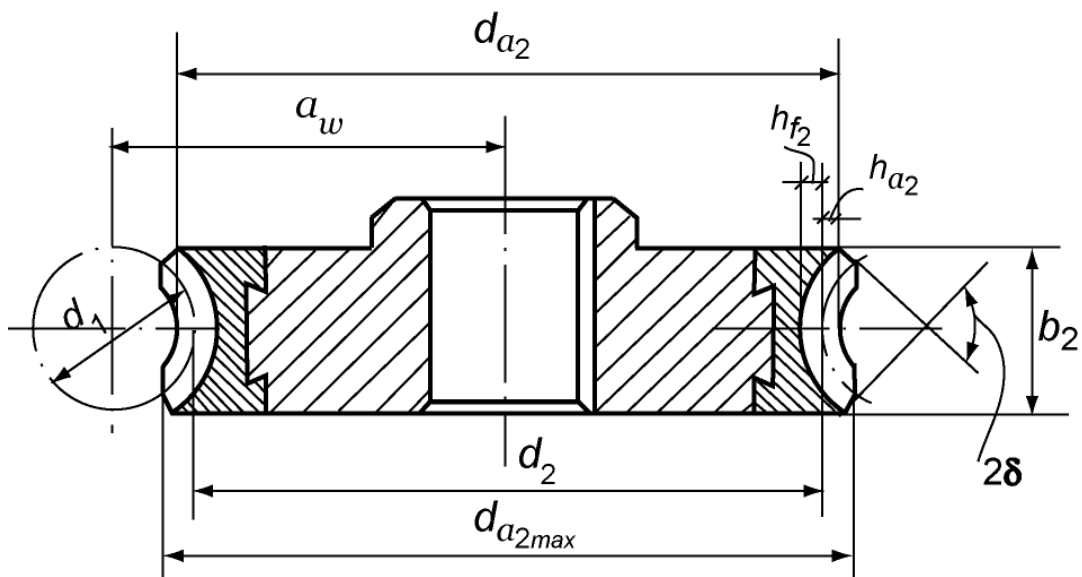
Основні геометричні розміри черв'ячного колеса:
